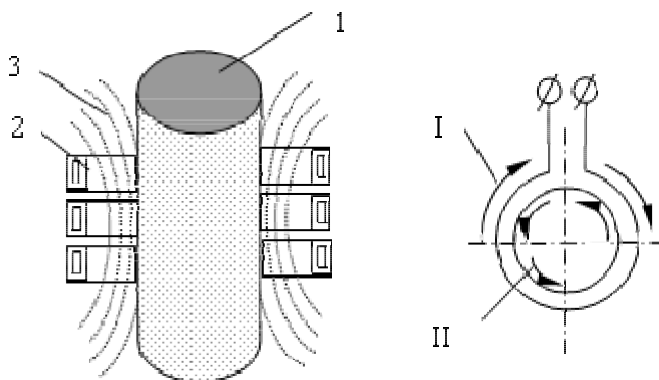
Схема нагрева токами высокой частоты: 1 – деталь; 2 – индуктор; 3 – магнитное поле; I – направление тока в индукторе; II – направление тока в детали
